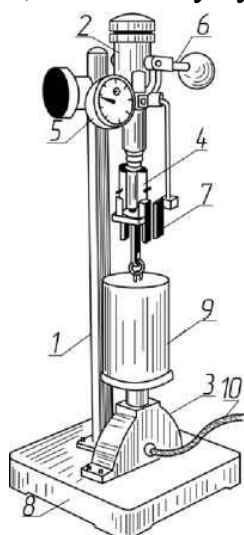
Прилад КИ-4273: 1 - стійка; 2 - кронштейн; 3 - штовхач; 4 - захват; 5 - індикатор; 6 - важіль з вантажем; 7 - шкала; 8 - основа; 9 - вантаж; 10 – ручка.
